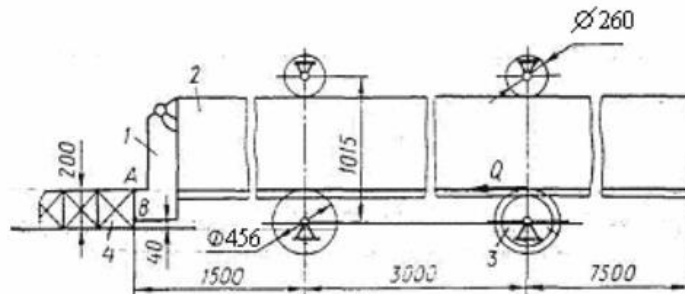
Здвоєний пічний рейковий штовхач: 1 - упор штанги; 2 - штанга; 3 - приводна шестерня; 4 – сляб
